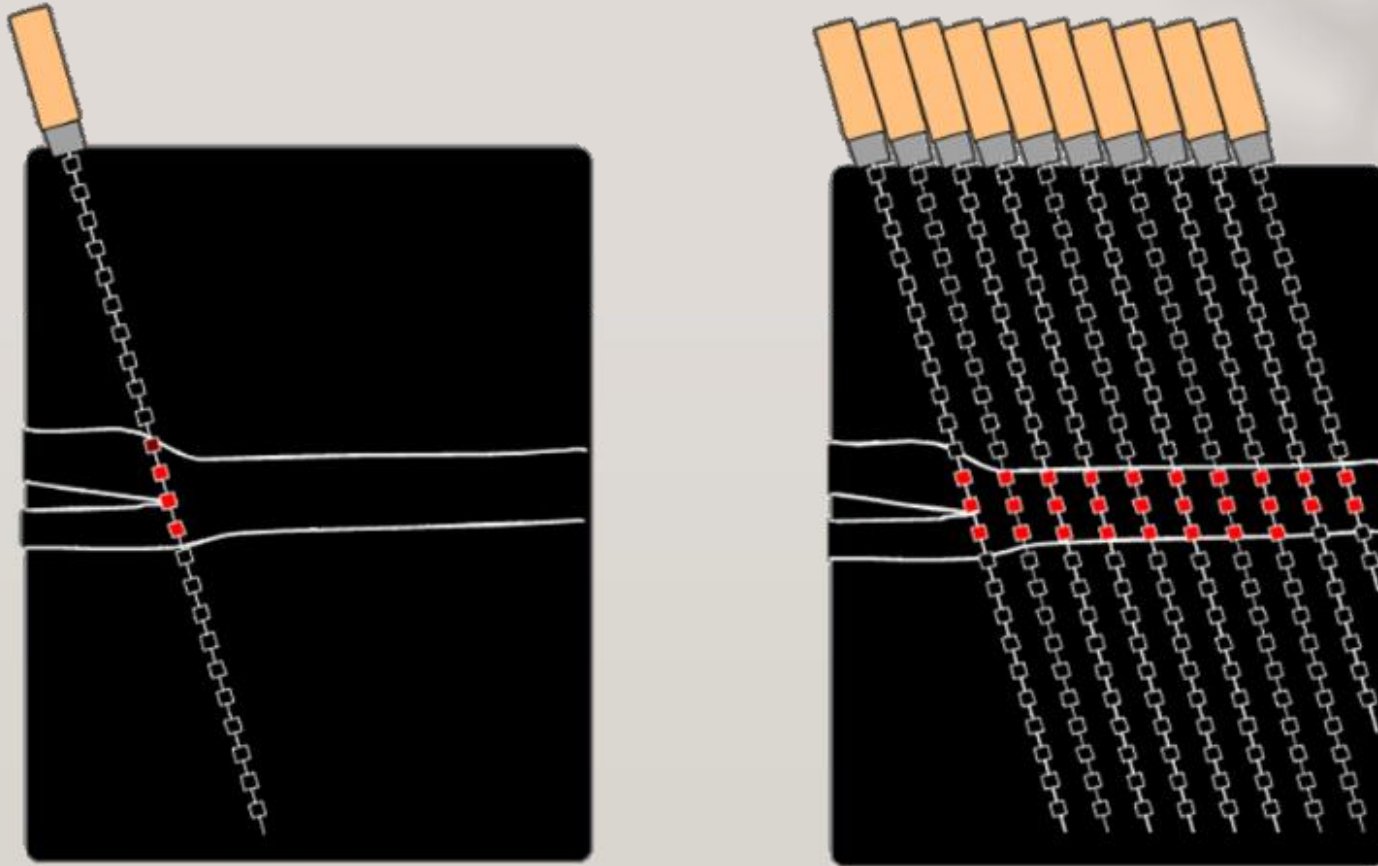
Exploration unidimensionnelle et bidimensionnelle
